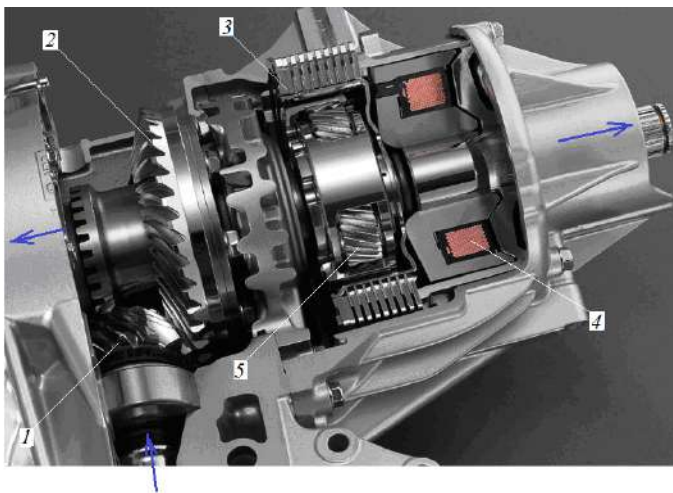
Підвищуюча передача трансмісії SH-AWD: 1 – корпус; 2 – гідропідтискаєна фрикційна муфта; 3 – сателіти планетарного ряду; 4 – головна передача; \rightarrow – напрямок руху потоку потужності
